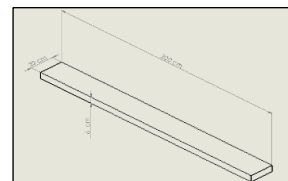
Plano Pieza 2: paleta Mecánica. Fuente:
